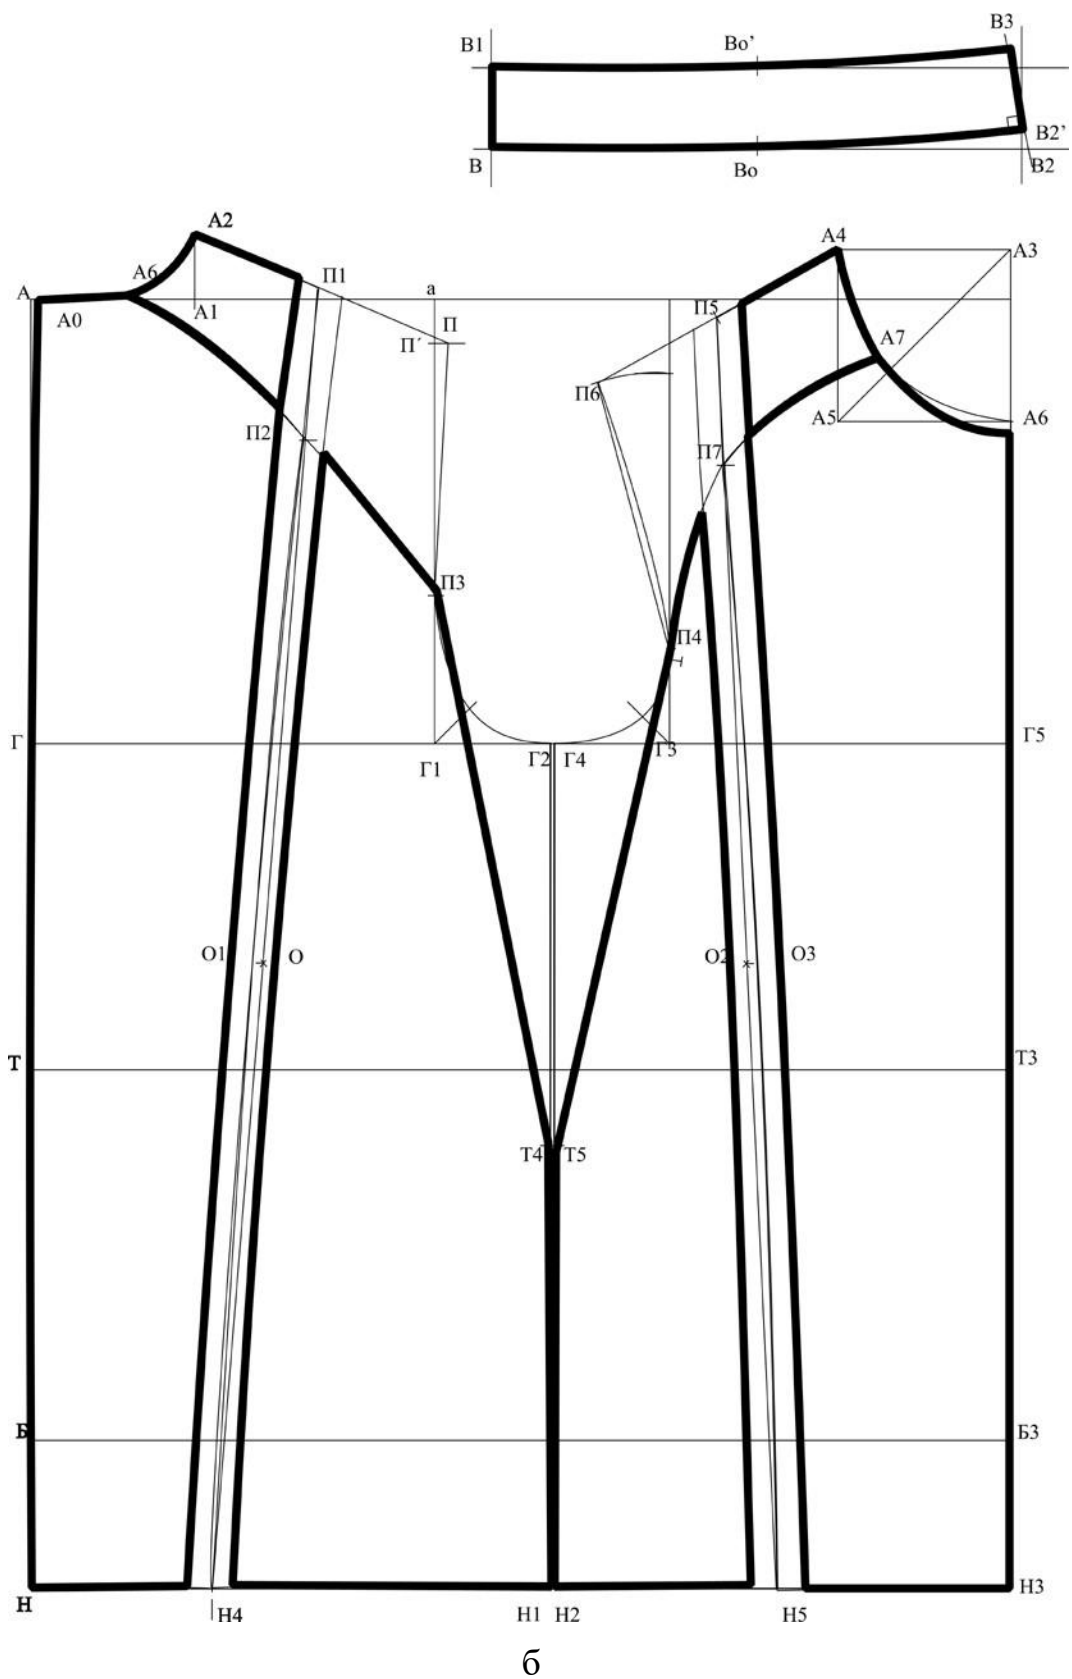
Схема кресленика базової конструкції куртки дитячої (пілочка, спинка, комір)
